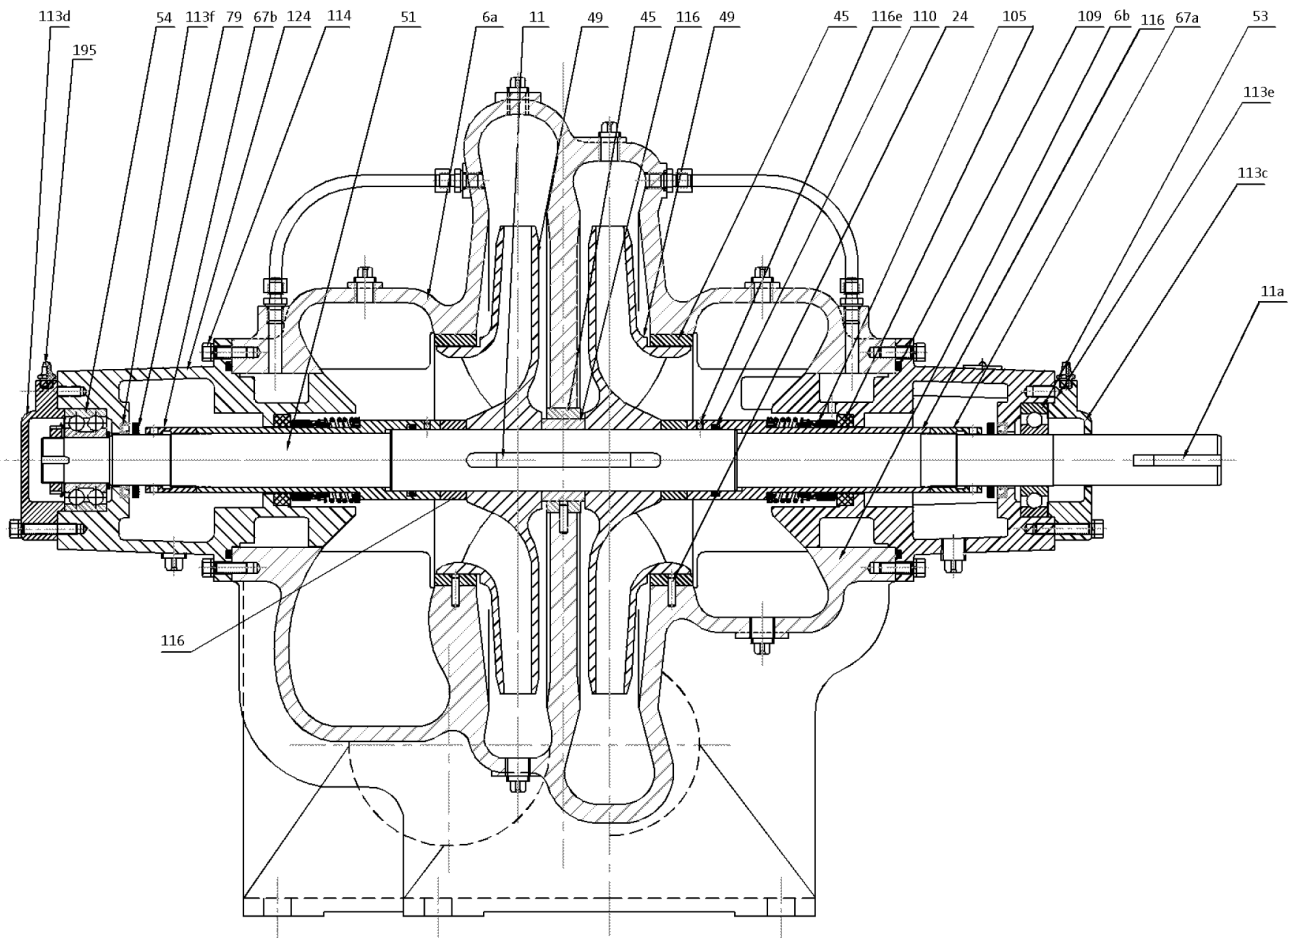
Вид в разрезе, тип конструкции 6, с торцевыми уплотнениями вала
